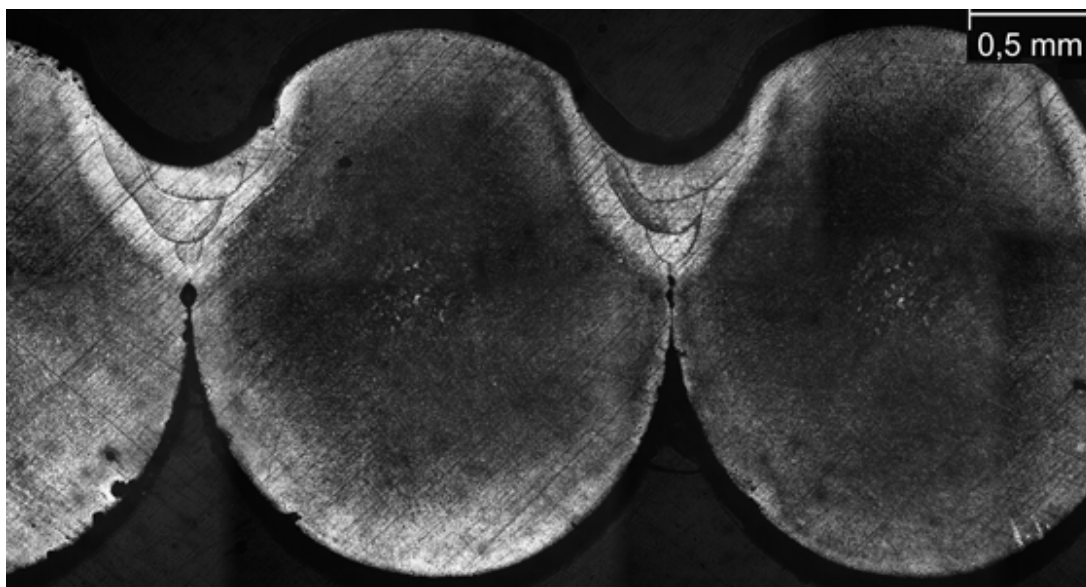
Общий вид области сварного шва пружинно-витого канала, полученного многопроходной сваркой импульсным лазерным излучением
